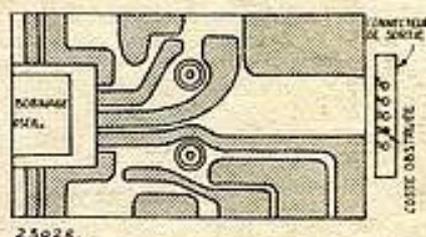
La plaquette de circuits imprimés du bloc BC 4, vue de dessus, côté soudage.
